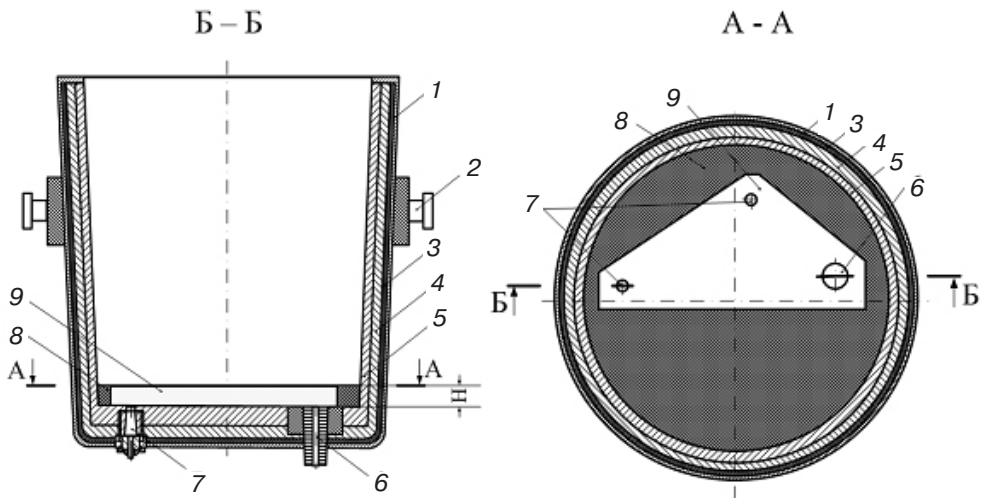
Схема сталеразливочного ковша с изменённой конструкцией футеровки дна (продольное сечение Б-Б, поперечное А-А): 1 – металлический корпус (броня), 2 – цапфы; 3-5 – слои огнеупорной футеровки соответственно: изоляционный, арматурный, рабочий; 6 – сталеразливочный стакан с шибберным затвором, 7 – аргонные пробки; 8 – выступ на футерованном дне из огнеупорного бетона, 9 – шаблон
